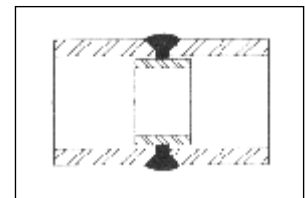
Soldadura de caño hecha con anillo de respaldo - corrosión severa
